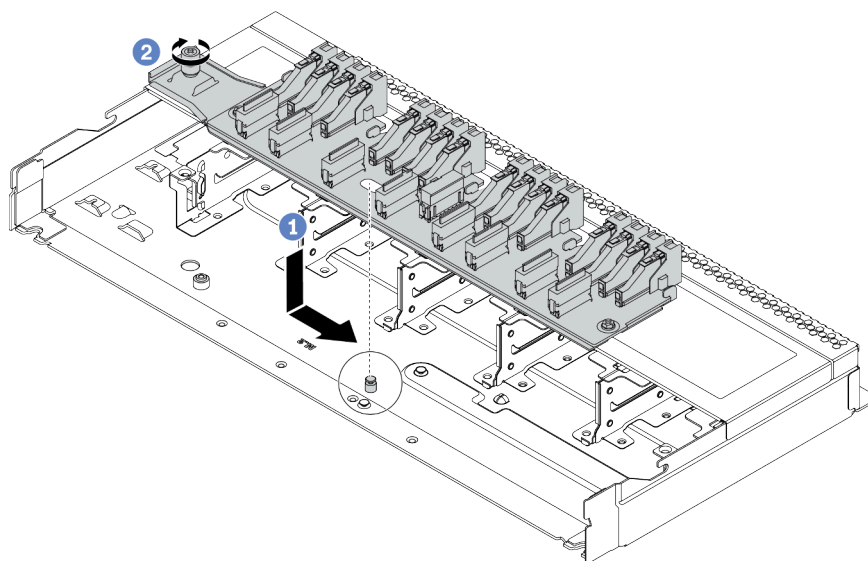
Installation d'un fond de panier pour 16 unités EDSFF
